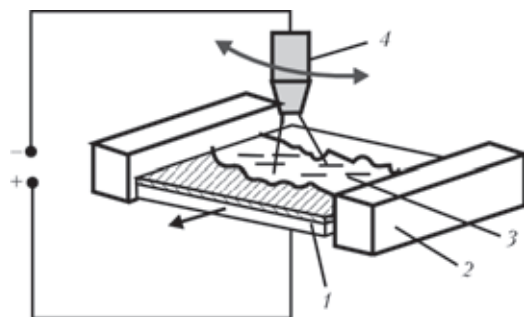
Схема работы плазменно-дуговой установки ОБ-1957: 1 — обрабатываемая заготовка; 2 — кристаллизатор; 3 — ванна жидкого металла; 4 — плазматрон
